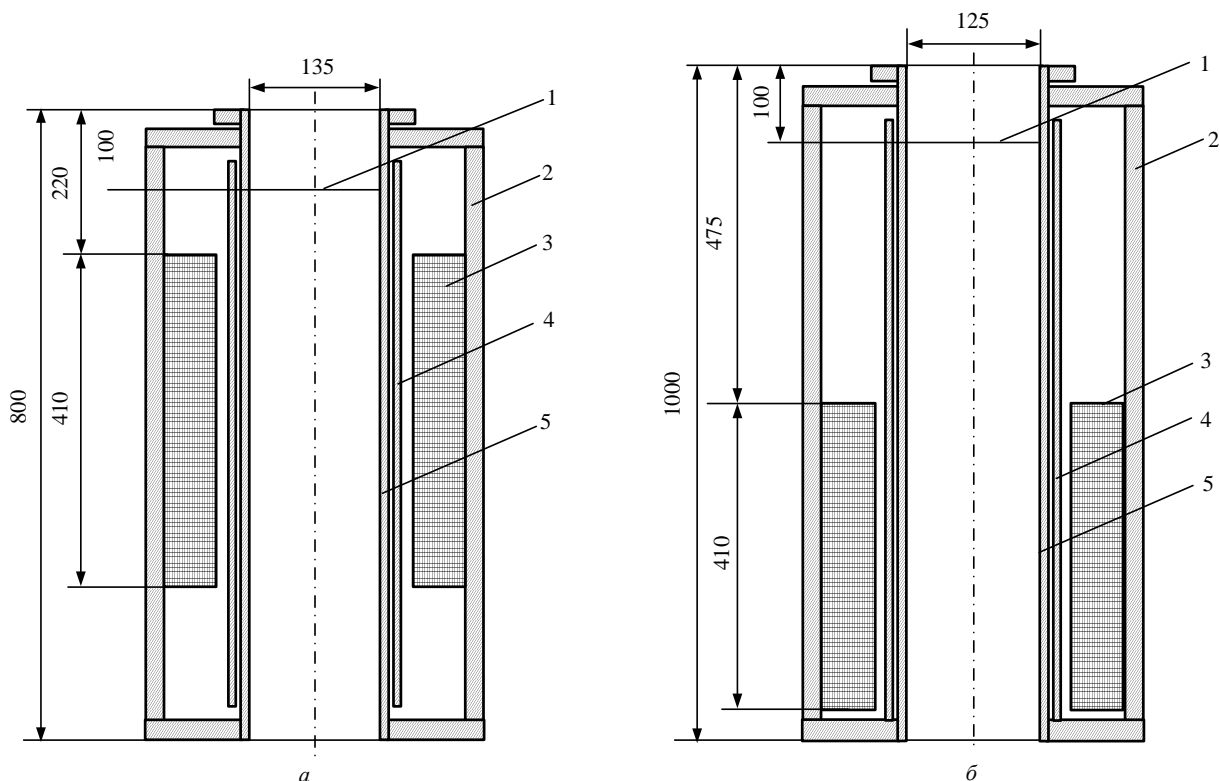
Схемы кристаллизаторов с ЭМП для отливки НЛЗ сечением 135×135 (а) и 125×125 (б) мм: 1 – мениск жидкого металла; 2 – корпус кристаллизатора; 3 – статор ЭМП; 4 – обечайка; 5 – гильза
